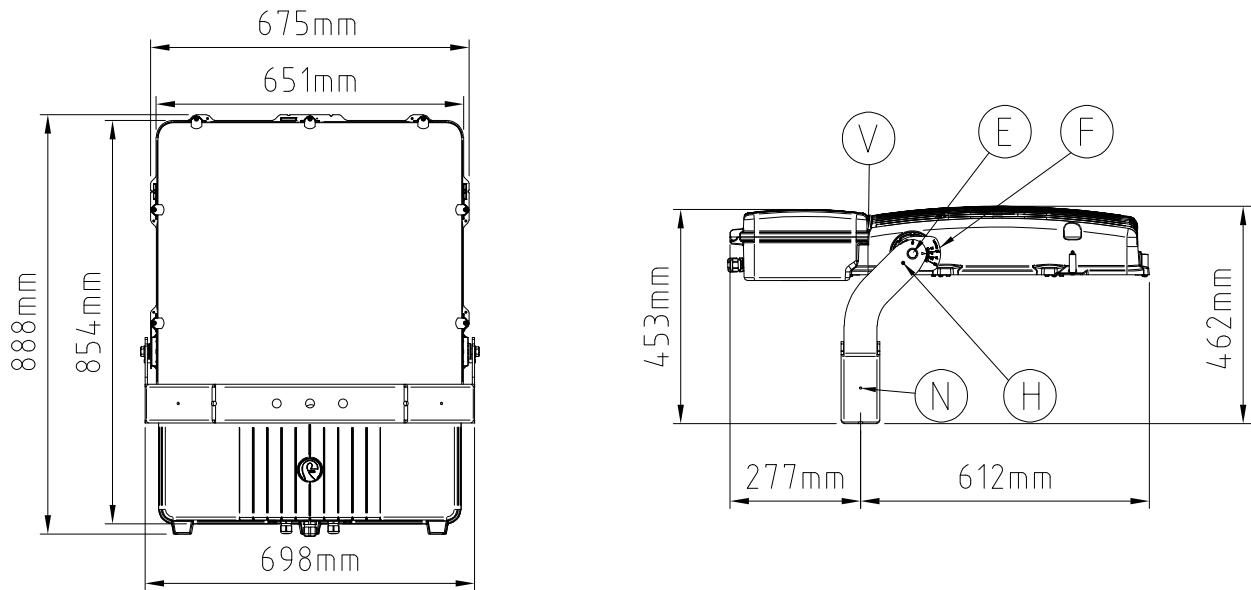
LEDMASTER ONE - Driver esterno a bordo 2 driver | *External driver on board 2 drivers
